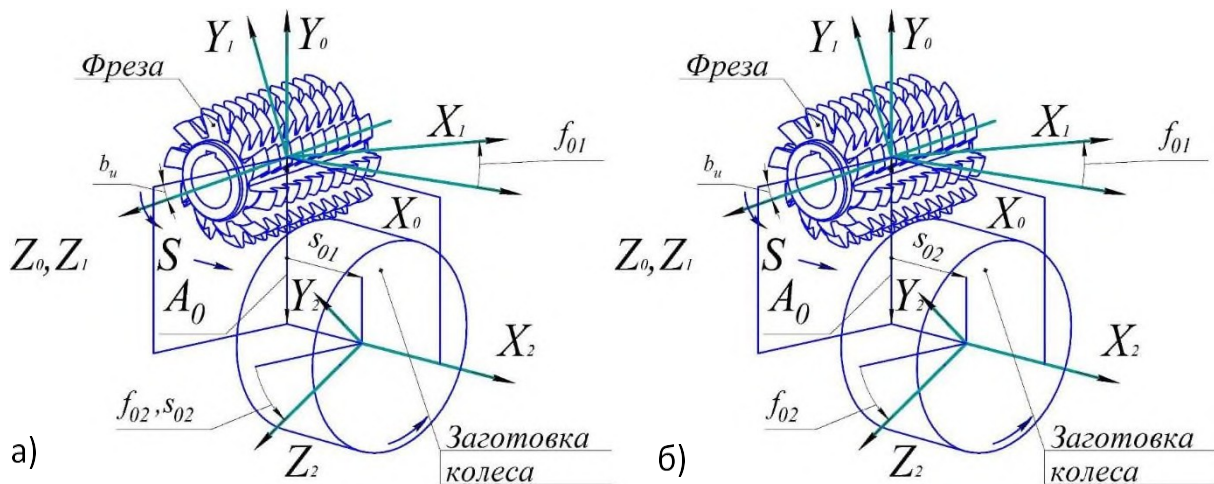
Розрахункова схема формоутворення циліндричних зубчастих коліс черв'ячними фрезами: а) косозубі колеса, б) прямозубі колеса
